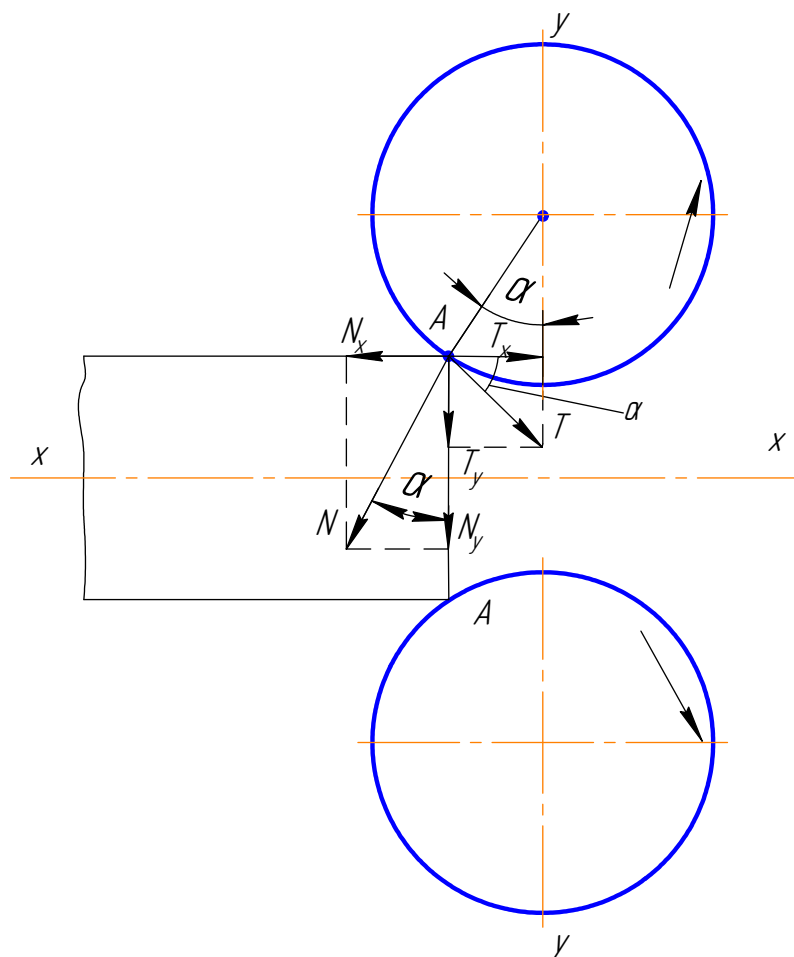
Условие захвата заготовки при неуставившемся процессе прокатки
